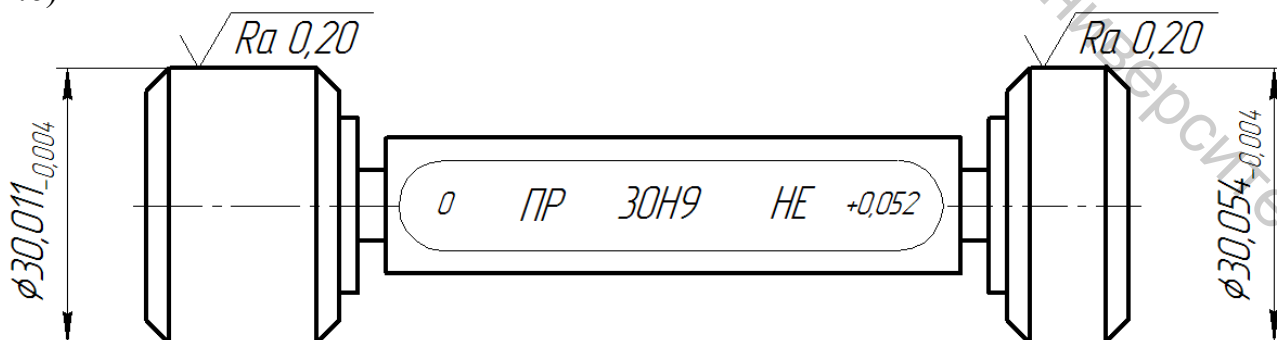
Эскиз пробки с элементами маркировки
